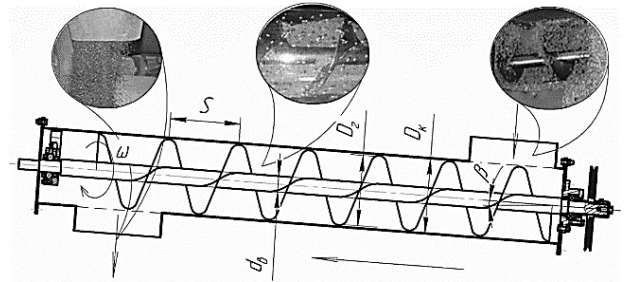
Схема роботи шнекового транспортера: β – кут нахилу шнека; ω – кутова швидкість робочого органу; S – крок гвинта; D_2 – діаметр гвинта; D_k – діаметр кожуха; d_0 – діаметр вала шнека
